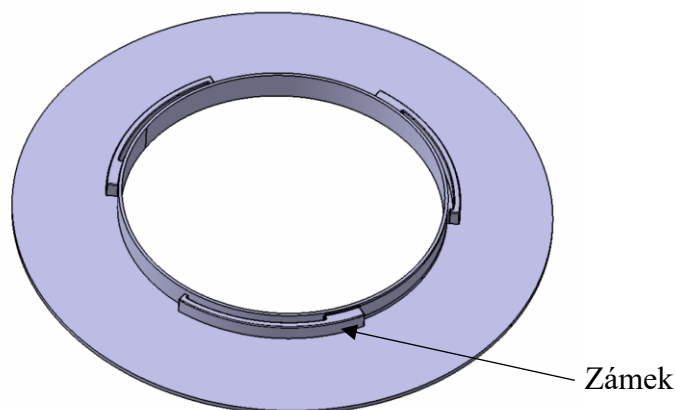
Koncepční varianta 2, detail zapadnutého zámku v kapse
